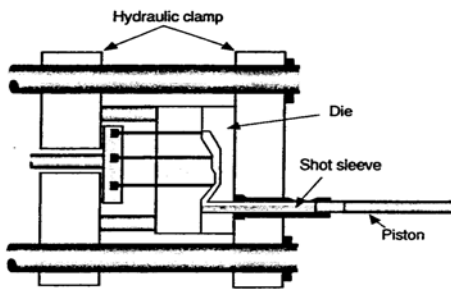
(a) Cold Chamber Die Casting [3] 冷室法
